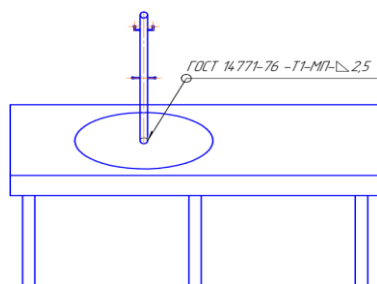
Сборка и сварка стойки с основанием
